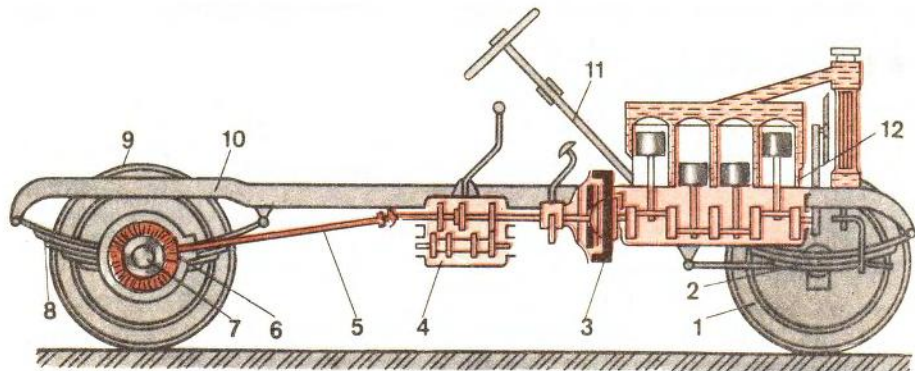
Расположение основных частей, их механизмов и деталей автомобиля:
